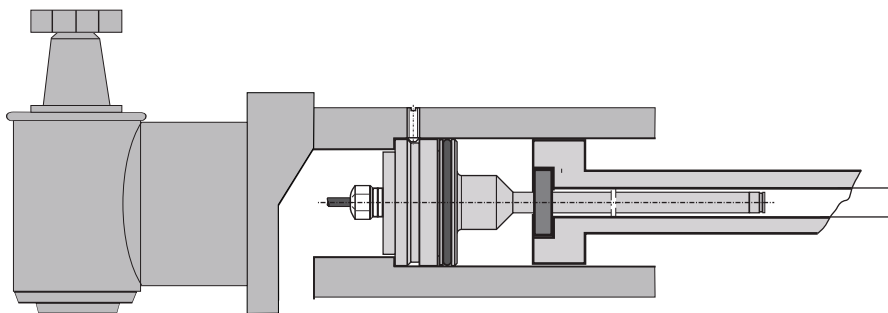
Capteur de déplacement BTL6-E500....E2/E28..., montage
